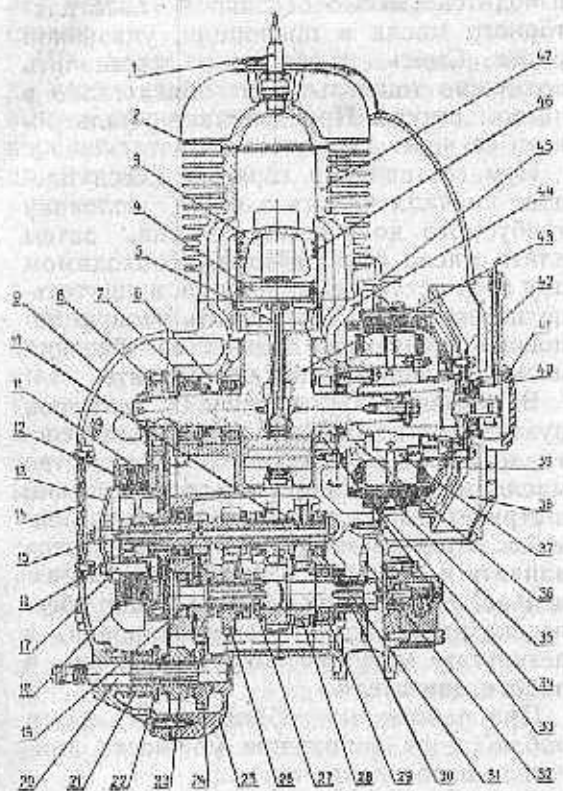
Блок двигателя с коробкой передач в разрезе:
